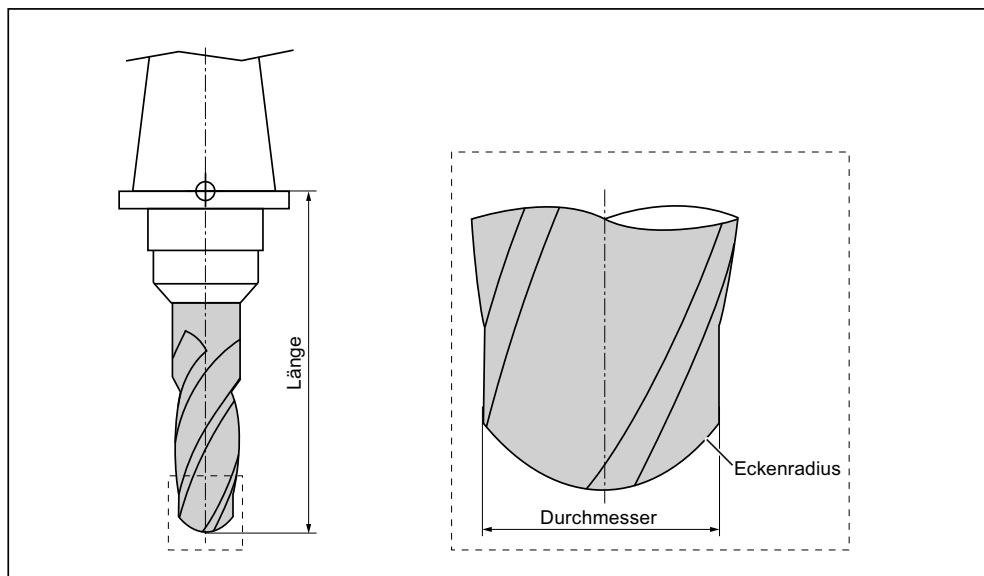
3D-Werkzeugtyp am Beispiel eines Kugelkopffräsers (Typ 111)
